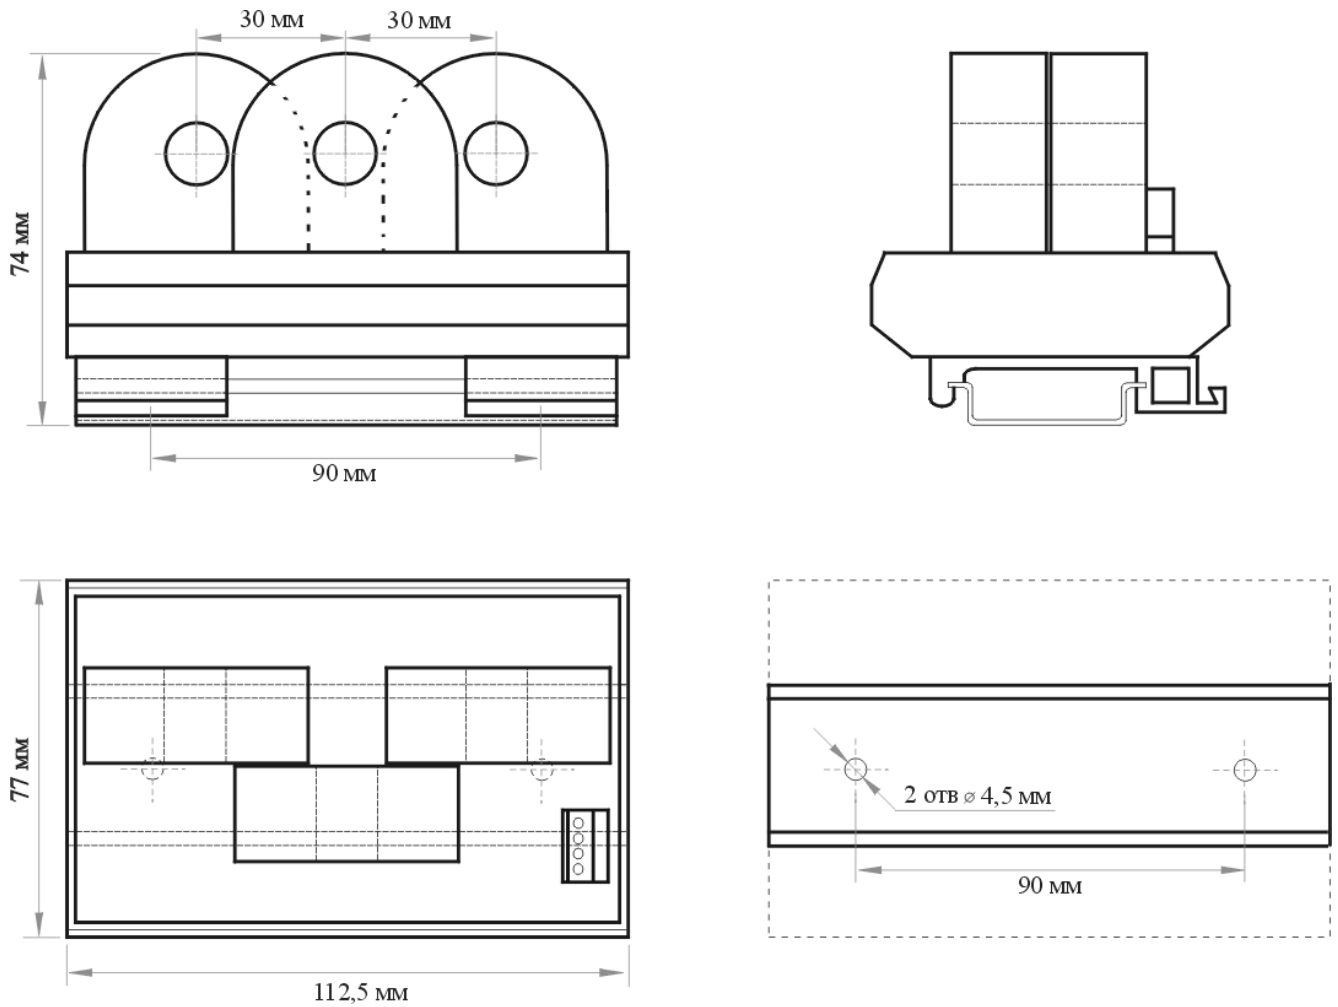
Габаритные размеры датчиков тока I-ой группы.
